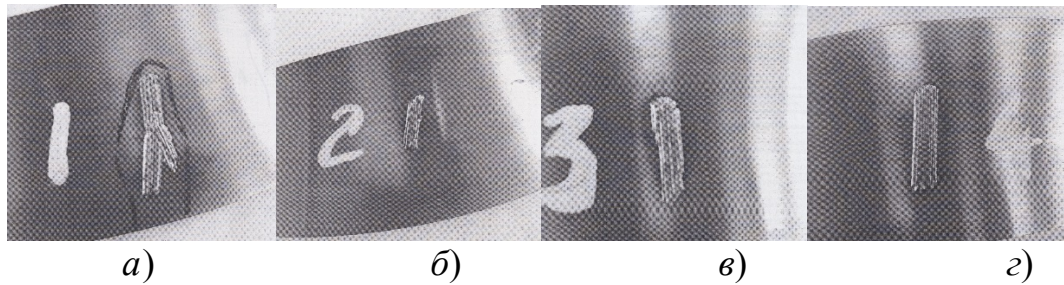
Внешний вид выборки трещины под лазерную наплавку
